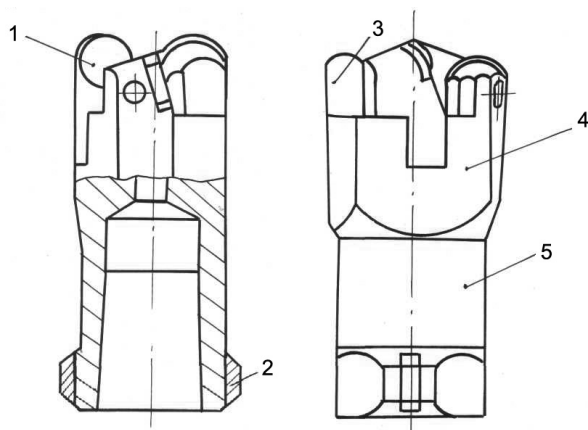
Долото для вращательного бурения шпуров: 1 и 3 – перья с алмазно-твердосплавными пластинами; 2 – стабилизатор; 4 – калибрующий элемент; 5 – корпус.
